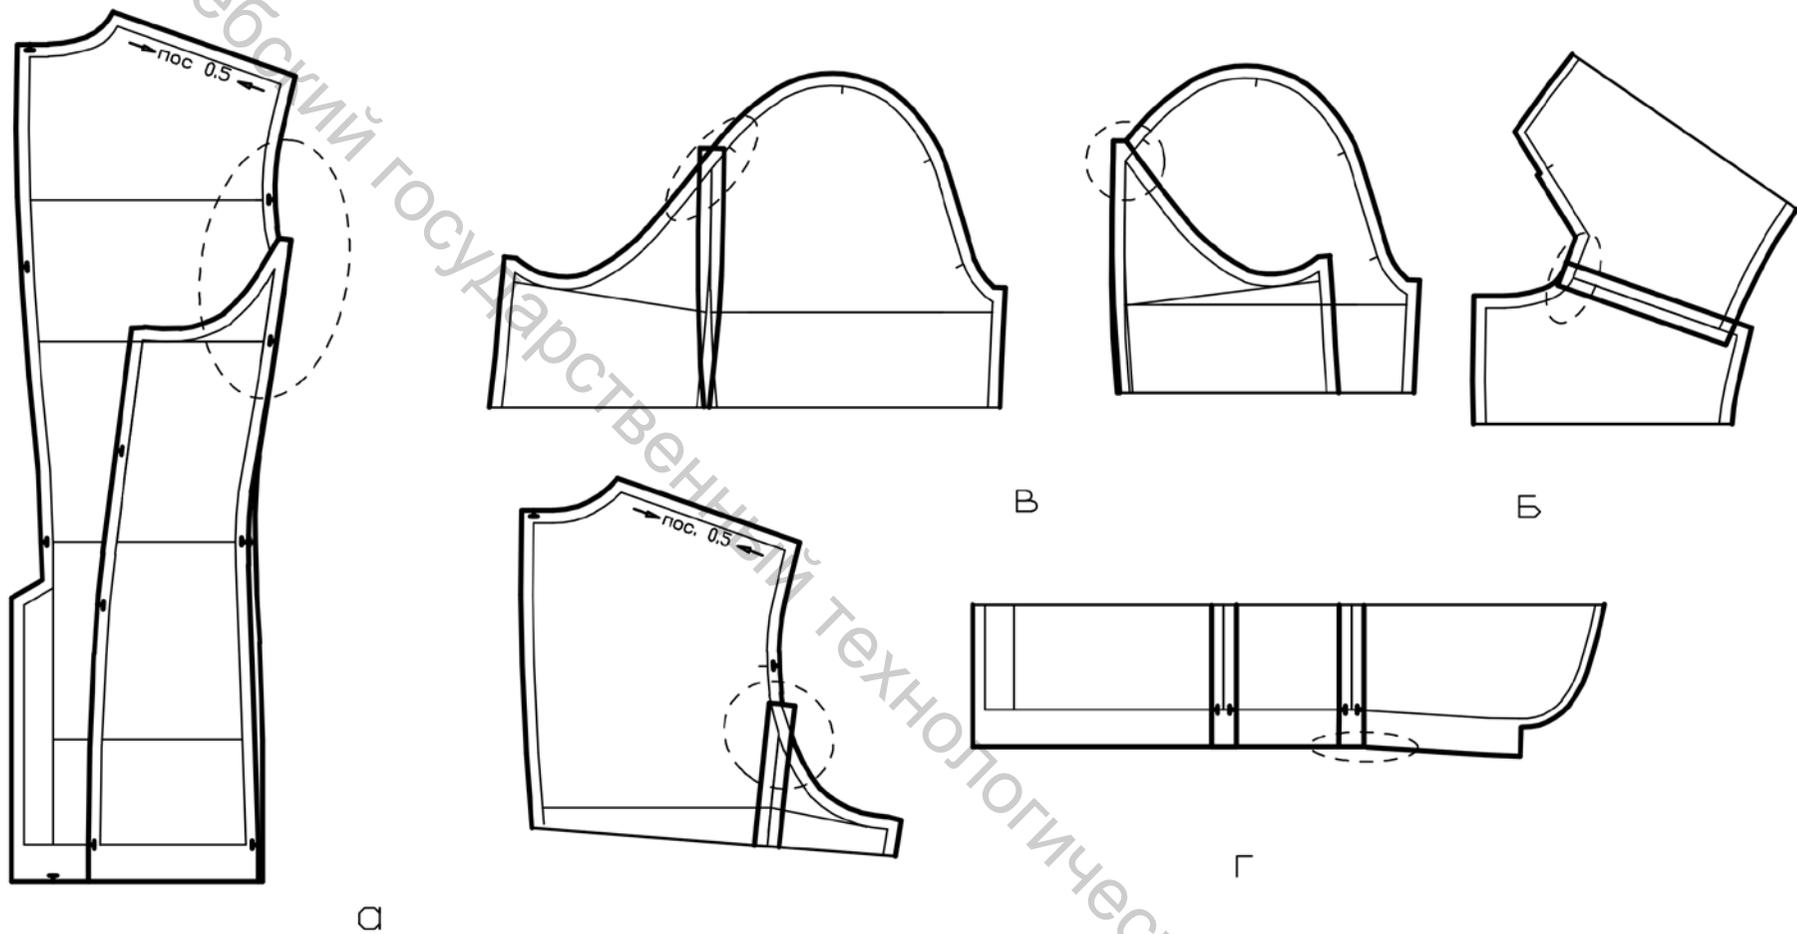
Примеры проверки сопряженности контуров деталей: а – спинки, бочка по боковым срезам; б – горловины спинки и переда; в – верхней и нижней частей рукава; г – низа изделия
